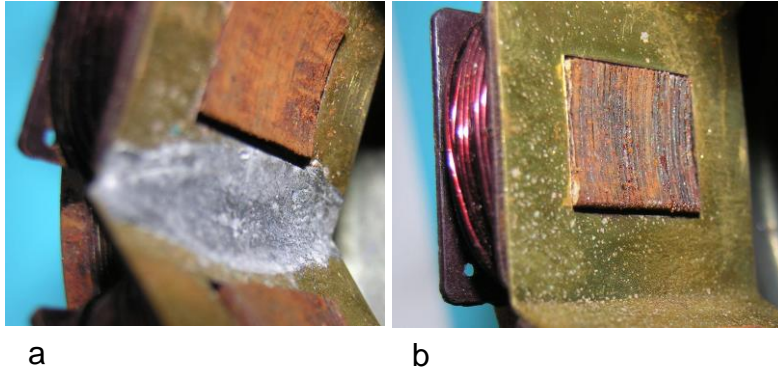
Befestigung der Ankerspulen mit einer Messingschablone:
